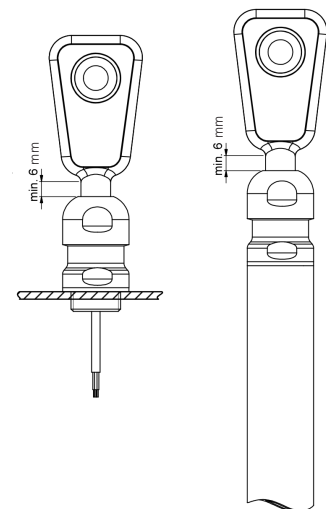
pms-Sensor D12-Adapterschaft mit Sensorverschraubung BF-pms/A1 befestigt am Maschinenteil oder am Edelstahlrohr D26.8 mit Innengewinde M20x1,5
